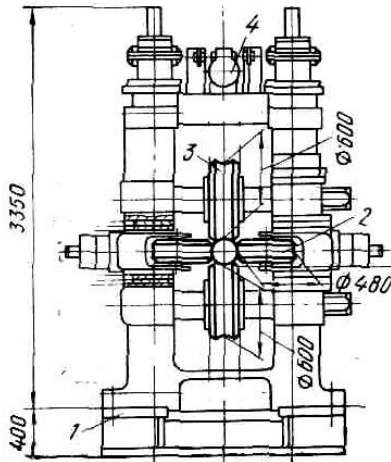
Зварювальна кліть для зварювання СВЧ
